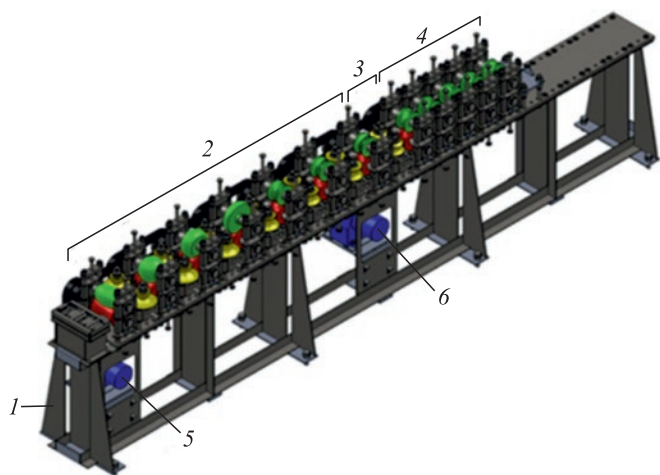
Общая компоновка «ТРЕНАЖЕРА-ТЭСА 10-50»: 1 – станина; 2 – формовочный блок; 3 – сварочный узел; 4 – калибровочно-профилировочный блок; 5 – привод формовочного блока; 6 – привод калибровочно-профилировочного блока
